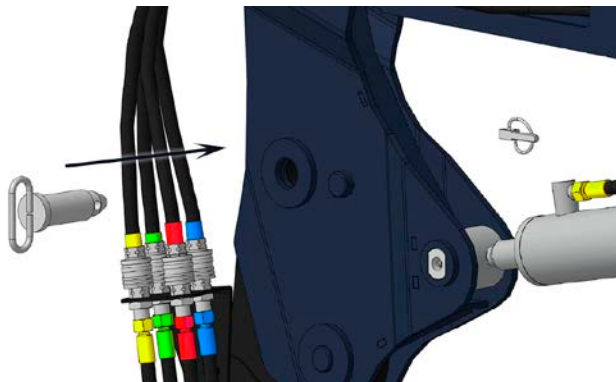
Вставка фиксатора (кроме Универсал Premium)
